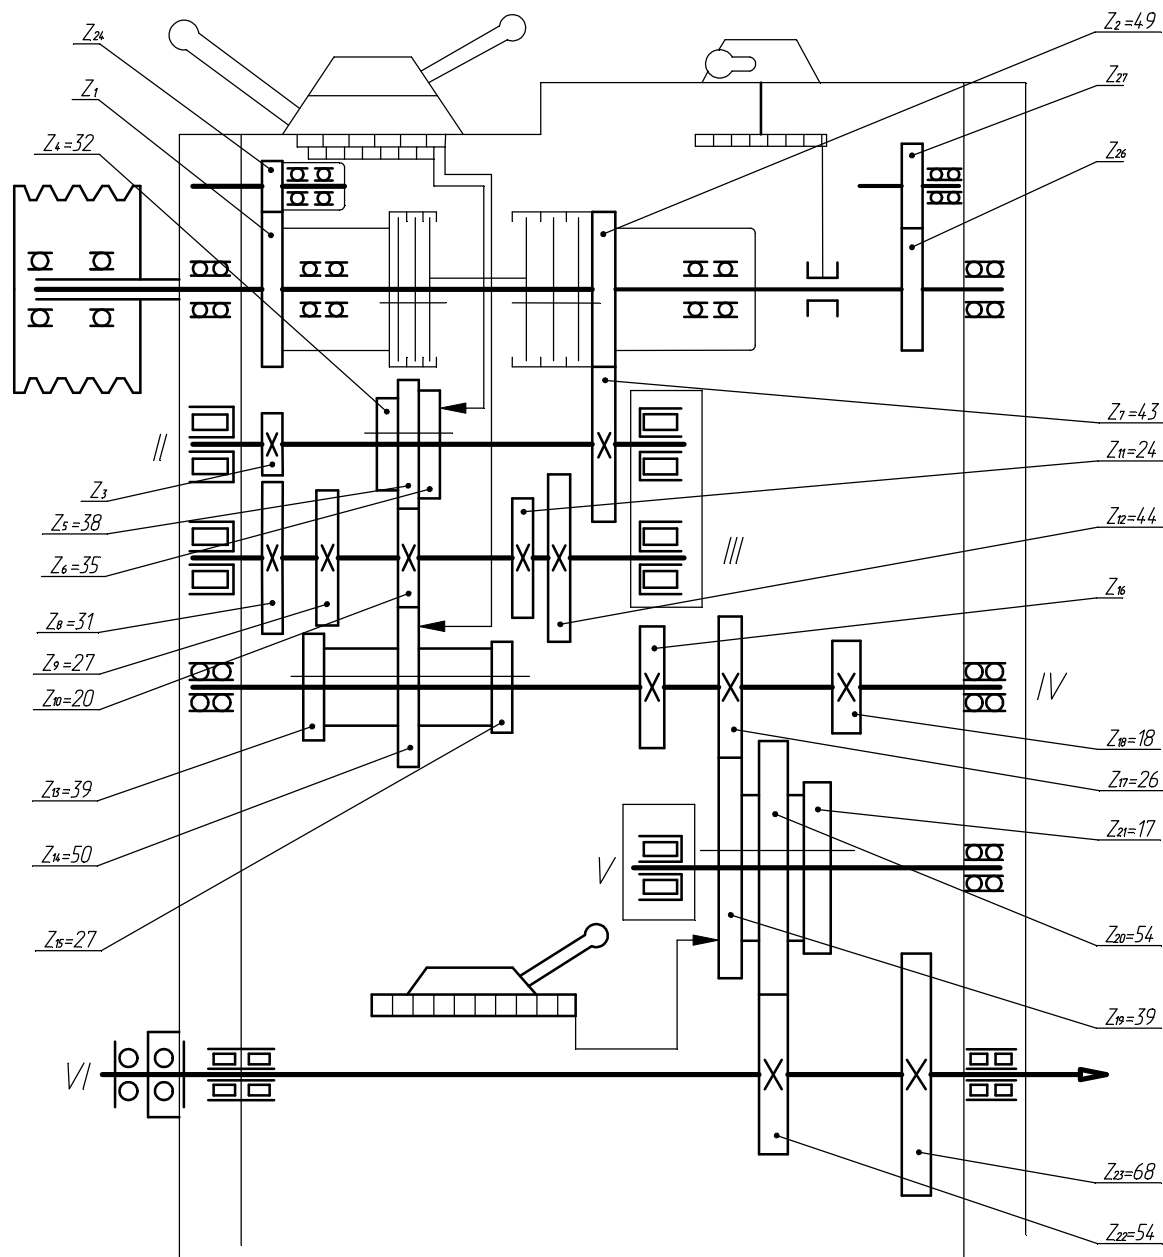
Кинематическая схема коробки скоростей главного движения универсального токарного станка CH-401
